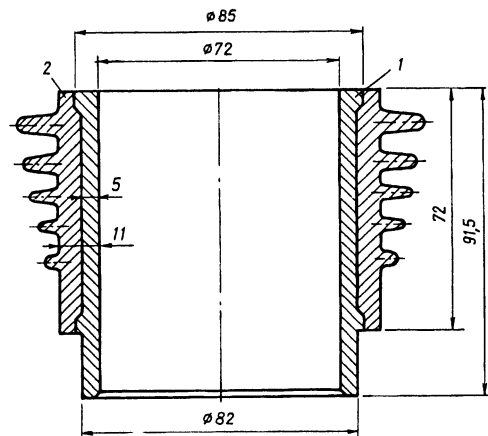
Биметаллический цилиндр пневмокомпрессора трактора "Беларус": 1 — чугунная вставка; 2 — алюминиевая рубашка
